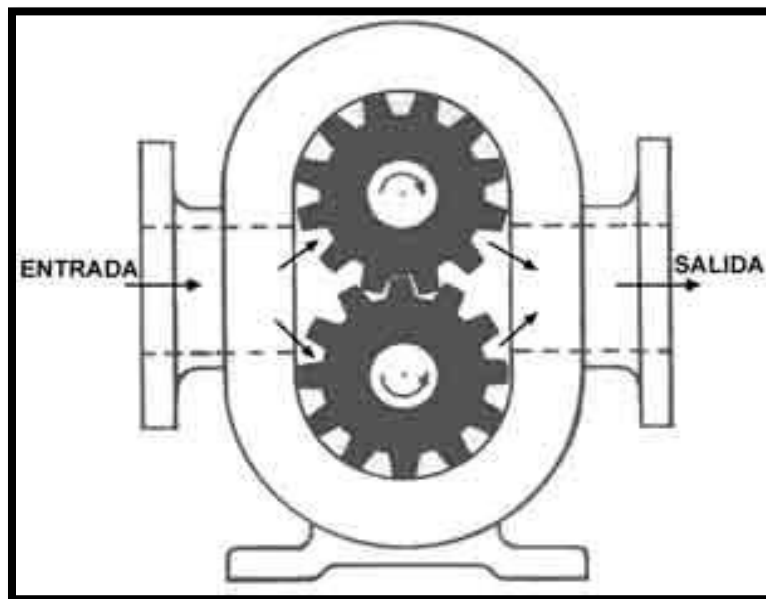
Diagrama de bomba rotatoria de engranajes
